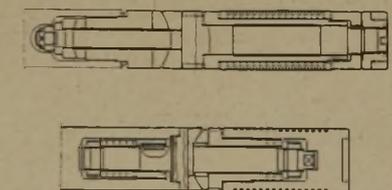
Gelenkig befestigte Kolben der 6. Stufe und verschiedenartige Ringausführungen
